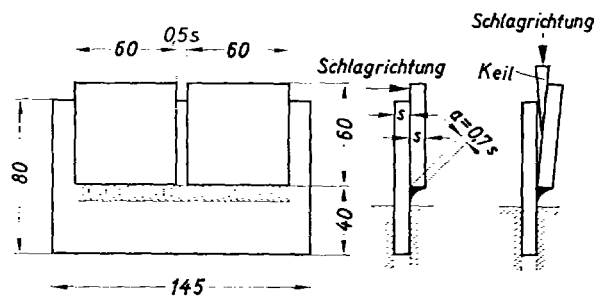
Keilprüfstück für Blechschweißer an $s \geq 4$ mm
